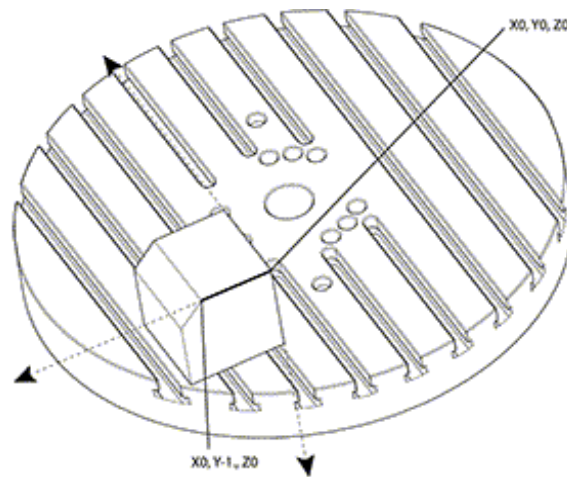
Základní umístění součástí ve souřadnicovém systému [11]
